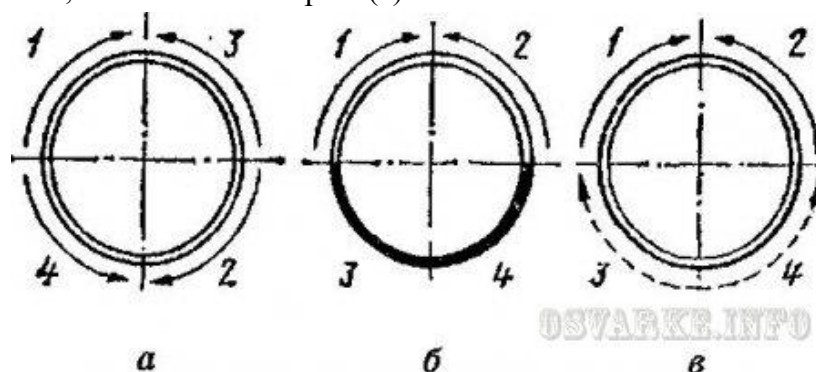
Последовательность сварки труб большого диаметра:
